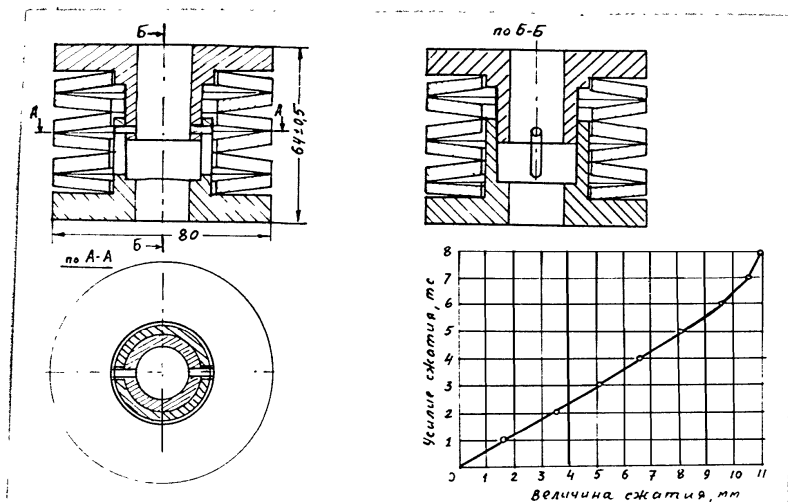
Динамометрическое устройство с тарельчатыми пружинами для длительных испытаний СПШ .
